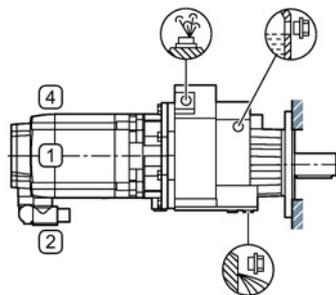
Einbaulagen für Stirnradgetriebe DF und ZF (Flansch-) oder DZ und ZZ (Gehäuseflanschausführung), Baugröße 29, 2-stufig und 3-stufig
